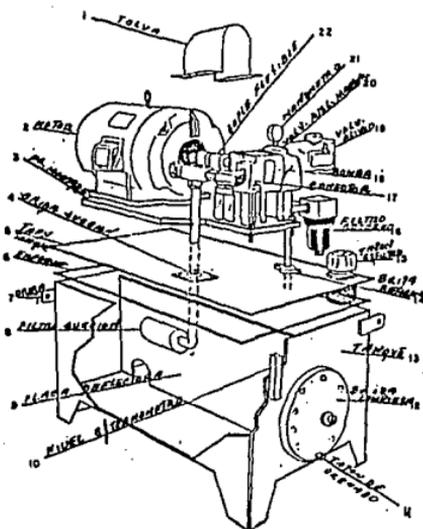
Partes componentes de la unidad de potencia hidráulica
